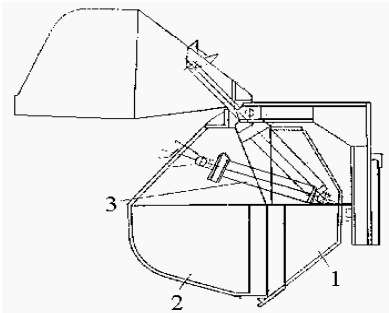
Ковш с верхним центром поворота бульдозерно-грейферной конструкции
